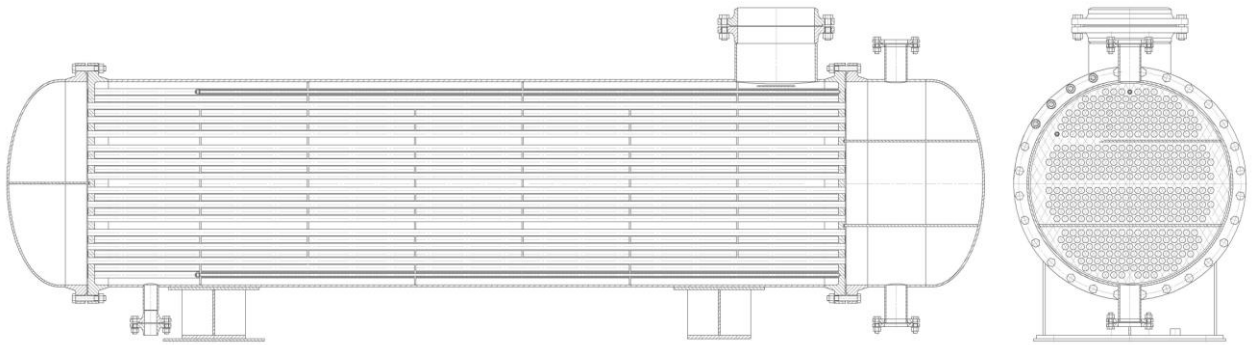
Схема проектного кожухотрубного конденсатора аміаку
